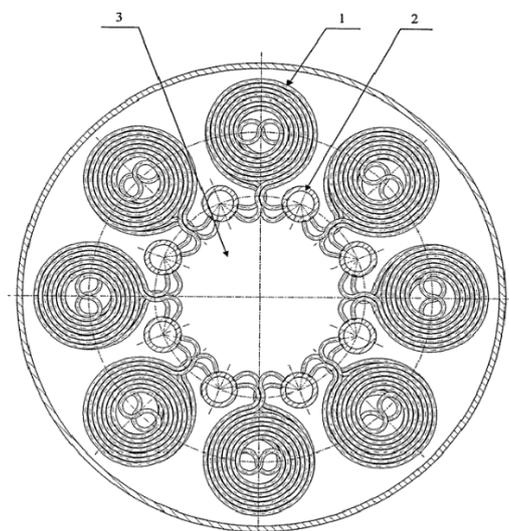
Трубная система коллекторного подогревателя высокого давления:
